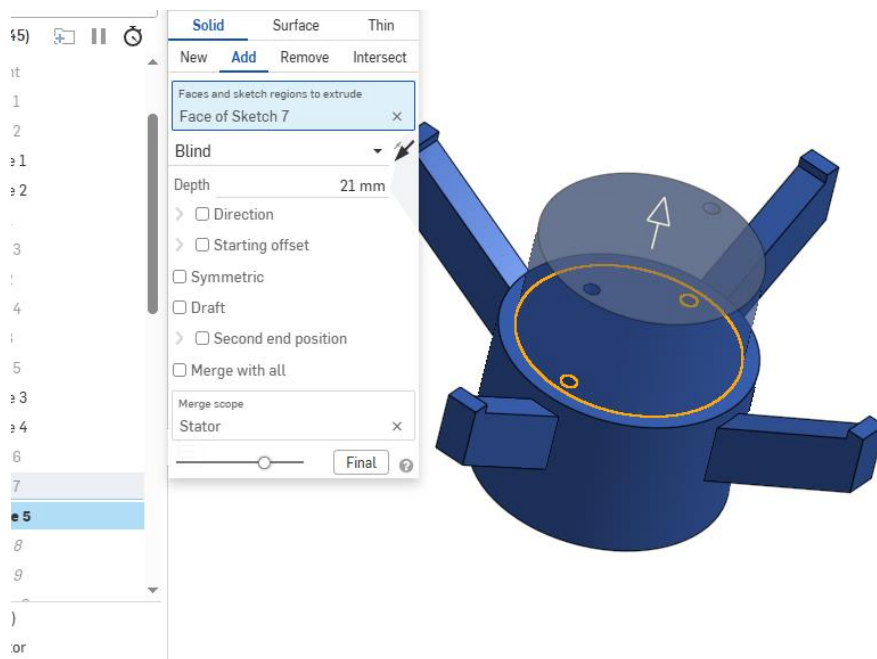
Витягування корпусу статора та побудова заднього обтічника ротора
